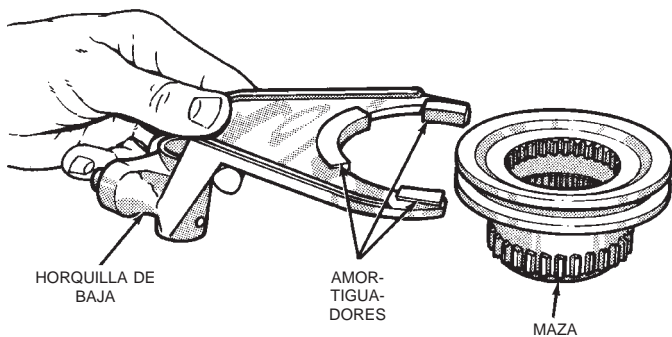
Ensamblaje de la horquilla de baja y la maza
